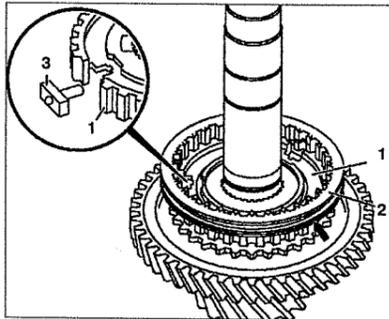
Снятие и установка роликового подшипника выходного вала: 1. Корпус сцепления, 2. Наружное кольцо роликового подшипника, 3. Фиксатор.
